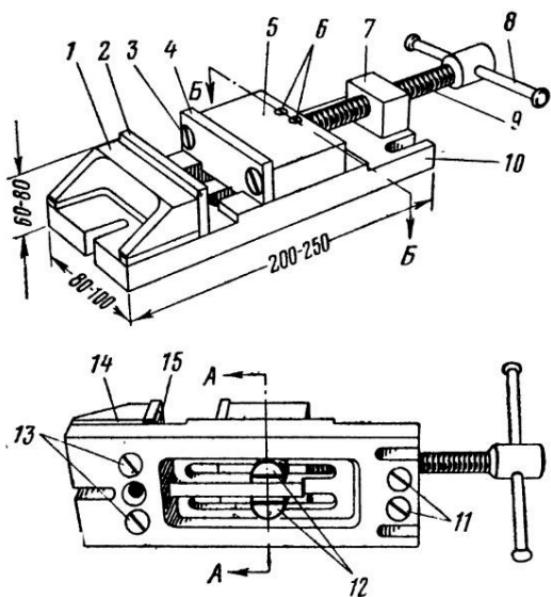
Тиски машинные: 1 — упор; 2, 4 — губки; 3, 15 — винты крепления губок; 5 — ползун; 6 — шпильки крепления винта; 7 — гайка; 8 — ручка; 9 — винт; 10 — основание; 11 — винты крепления гайки; 12 — винты крепления ползуна; 13 — винты крепления упора; 14 — подкладка.
